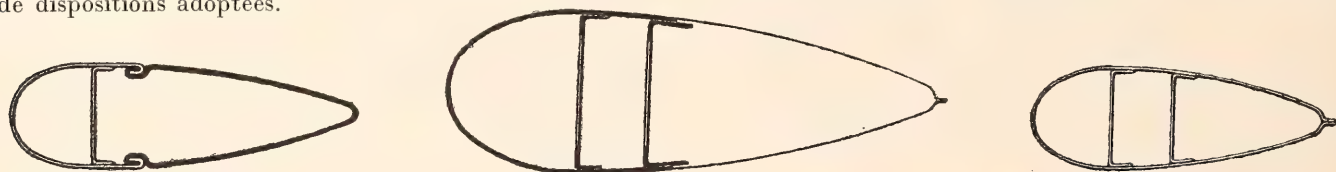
, 16, 15 (de gauche à droite). — Quelques profils fuselés de mâts et de poutres d'étau.
